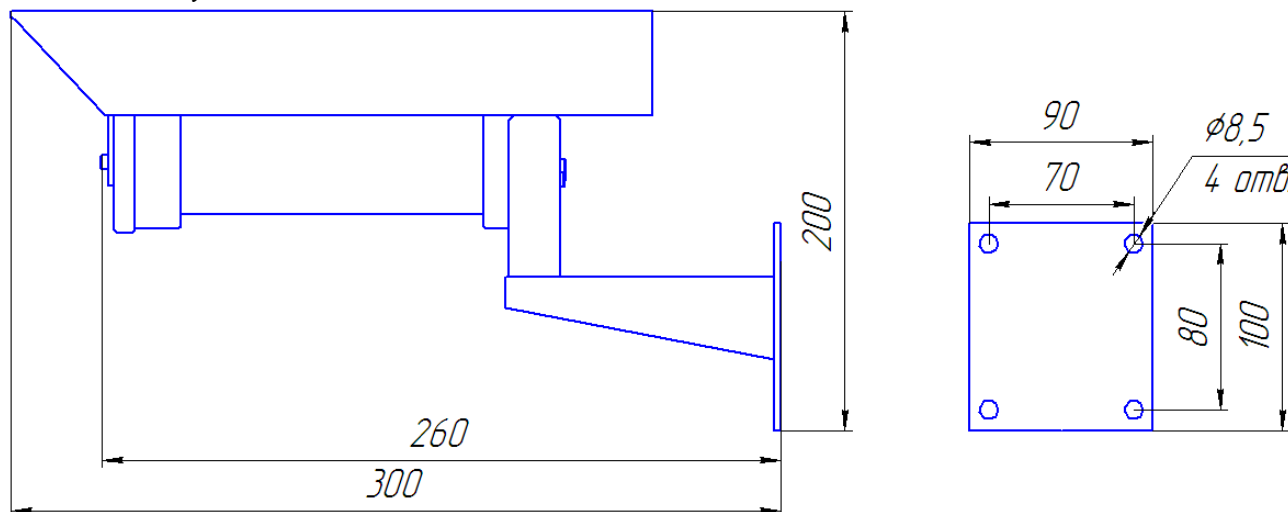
Габаритные размеры извещателя с крепежно-юстировочным устройством
